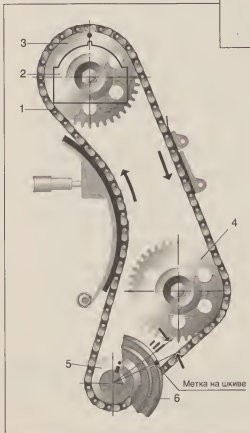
Положения меток при изношенной цепной передаче: 1 — цепь; 2 — корпус распределителя; 3, 4 — звездочки с 38 зубьями; 5 — звездочка коленвала с 19 зубьями; 6 — шкив.
